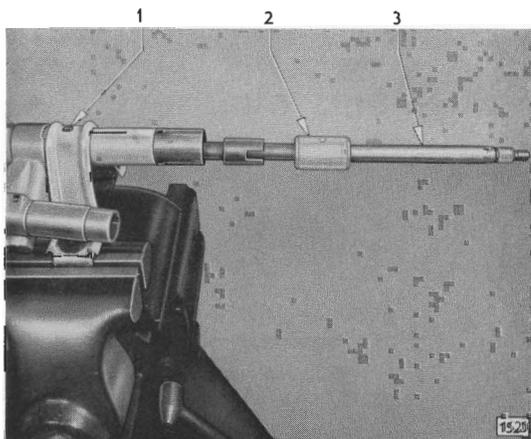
Lenkspindel mit Buchse aus Lenkstützrohr herausziehen
